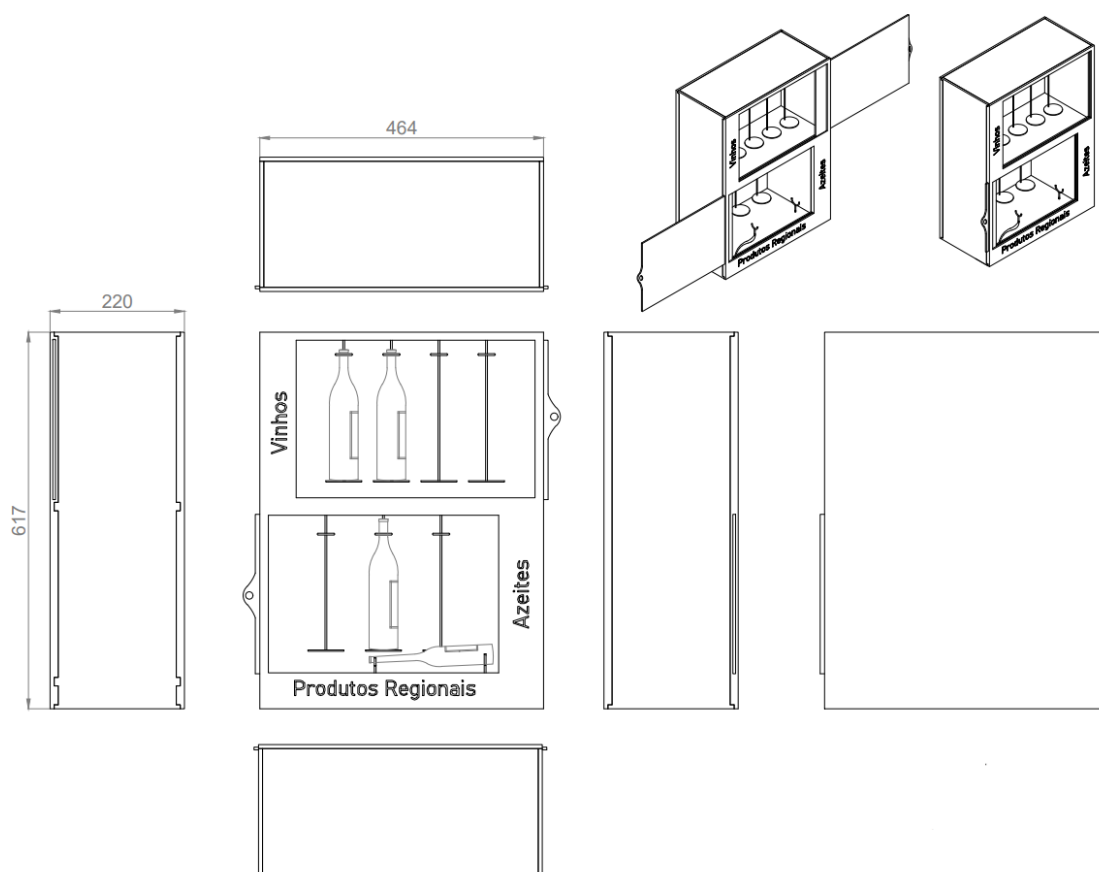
Desenho Técnico de Conjunto, Fonte: Autor
